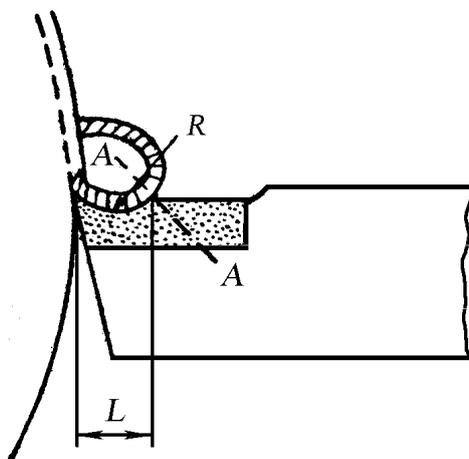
Схема режущей части резца с канавкой для ломания стружки при скоростном резании сталей
